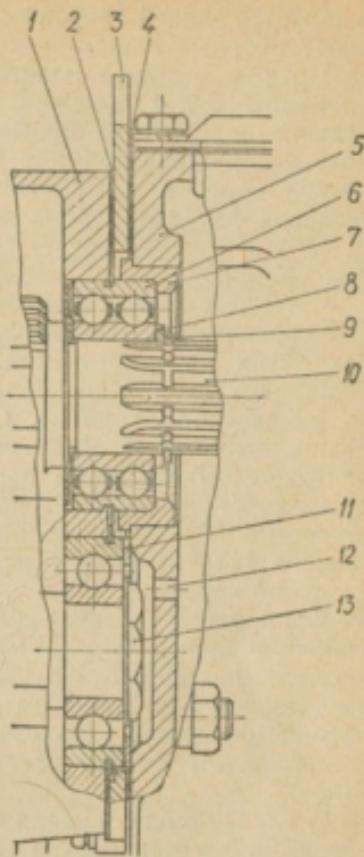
Соединение коробки передач с раздаточной коробкой:
